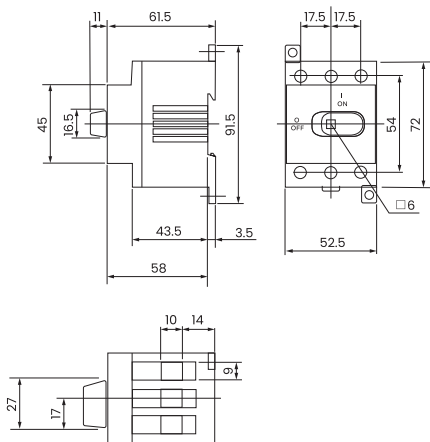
Габаритные и установочные размеры рубильников 63-80А ЗР
